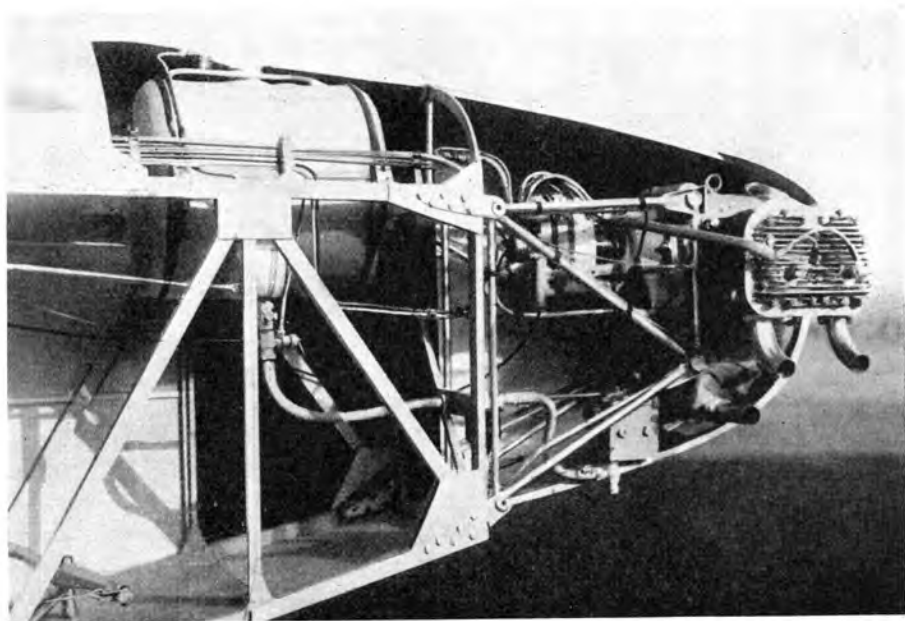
Motorträger der Klemm für Radialmotoren.
